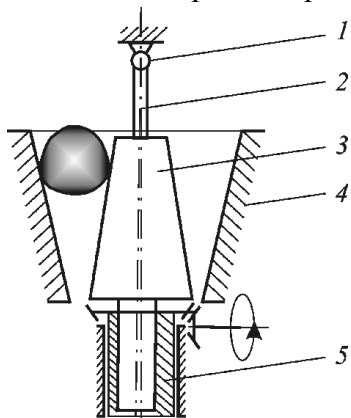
Схема конусной дробилки крупного дробления: 1 — узел подвеса подвижного конуса; 2 — вал; 3 — подвижный конус; 4 — неподвижный конус; 5 — эксцентриковый стакан
